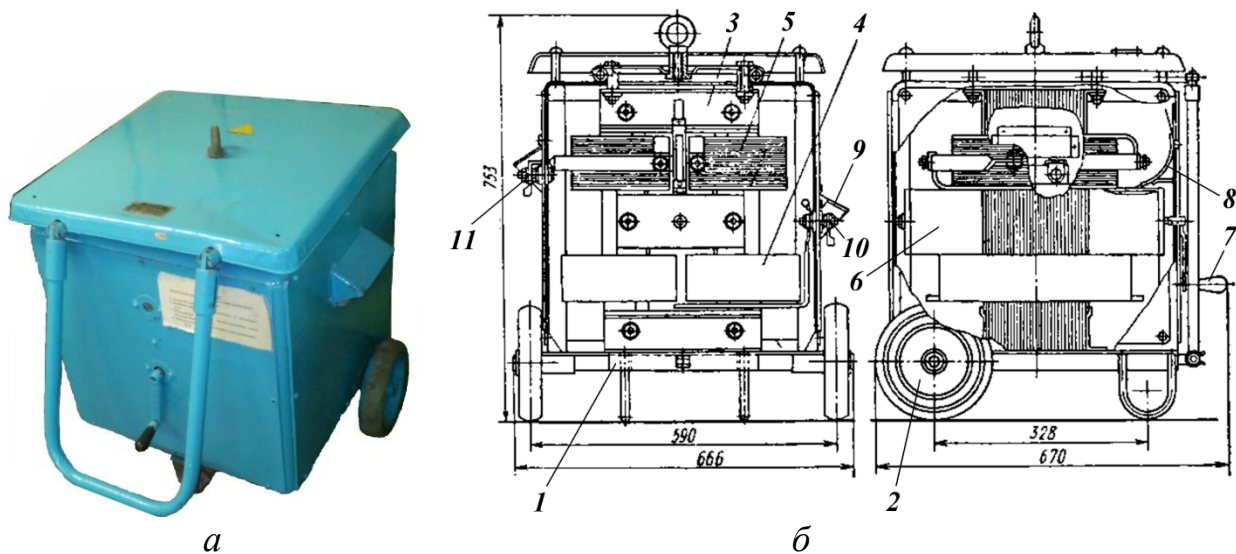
Трансформатор СТШ-500: *а* – внешний вид; *б* – конструкция; 1 – рама; 2 – колеса; 3 – магнитопровод; 4 – первичная обмотка; 5 – вторичная обмотка; 6 – магнитный шунт; 7 – ручка; 8 – указатель величины сварочного тока; 9 – кожух; 10 – клемник высокой стороны; 11 – клемник низкой стороны
